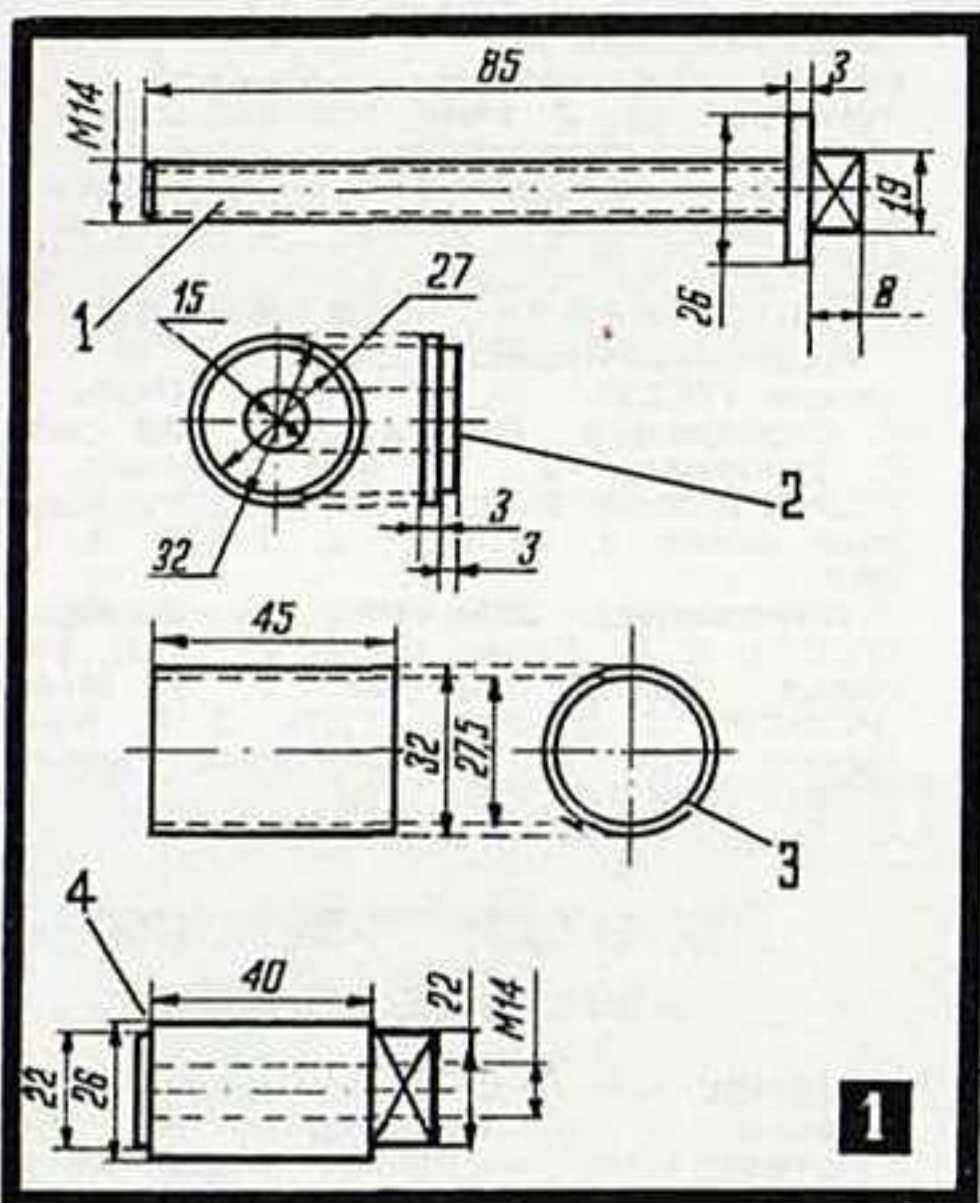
Детали приспособления: 1 — болт; 2 — шайба; 3 — трубка; 4 — специальная гайка.
